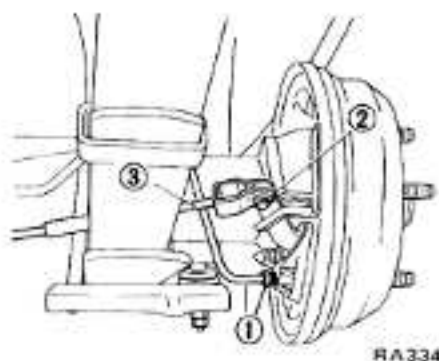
Dépose du tube de frein et du câble du frein à main
